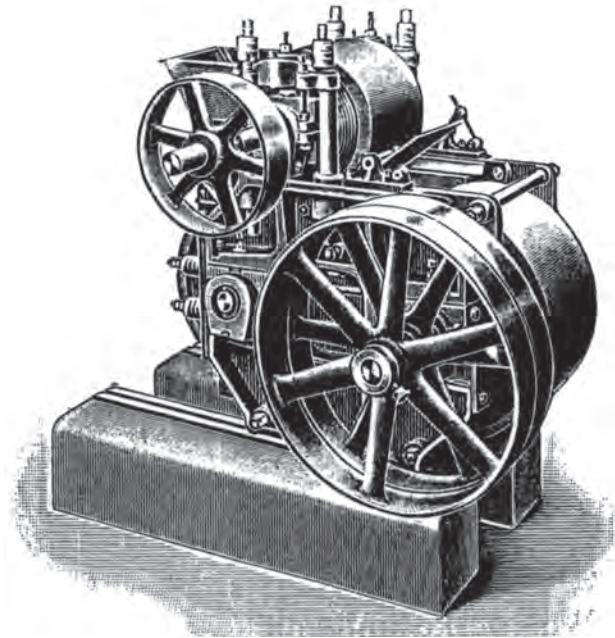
Dreiläuferwalzwerk mit drei Walzen für zweimaligen Materialdurchgang
